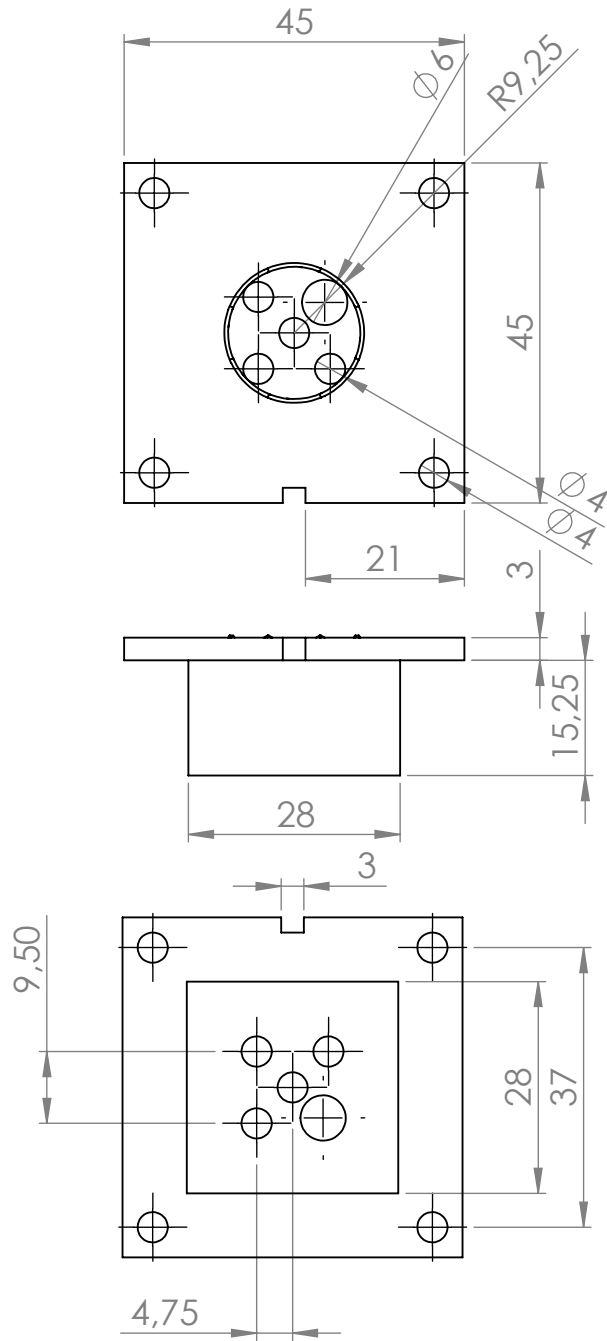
Diseño del molde para enmallado interno del Robot Rotador parte B
